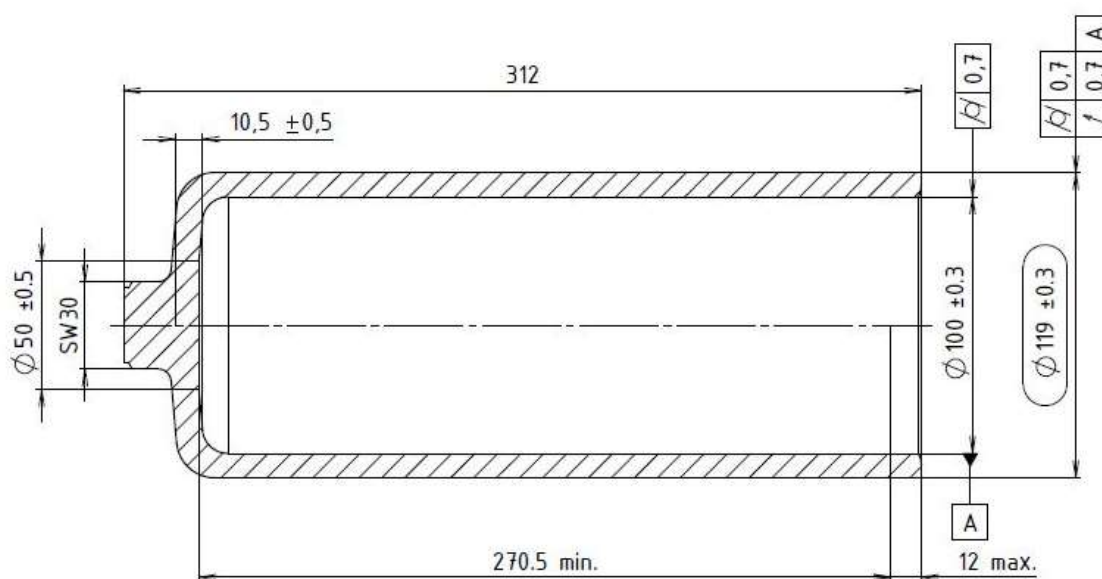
Umístění pouzdra tlakového filtru [7], [8]
